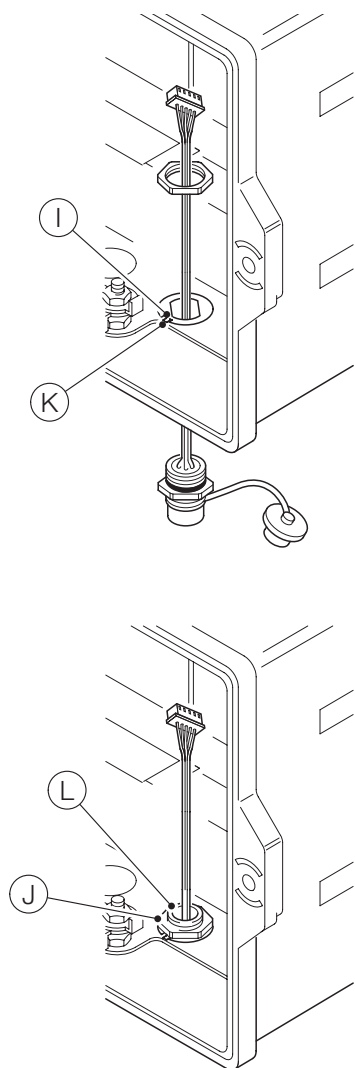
Fissaggio del gruppo cavi del connettore EZLink
